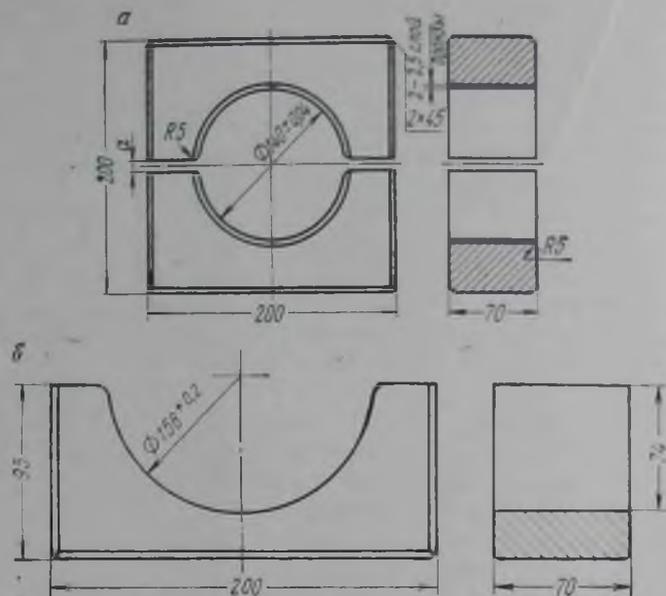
Призма для рихтовки плунжера гидровинтовой стойки:
